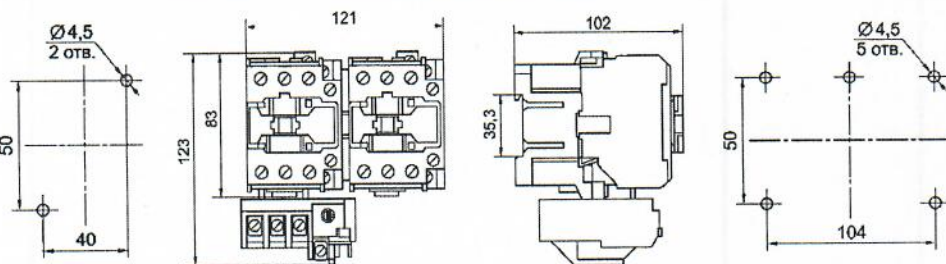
Пускатель реверсивный ПМ12-040 40А.
